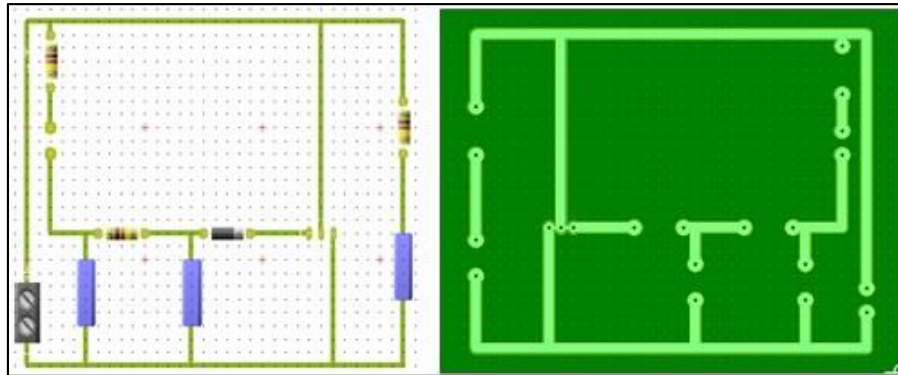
Diseño de las pistas en PCBWizard y en Copercam
